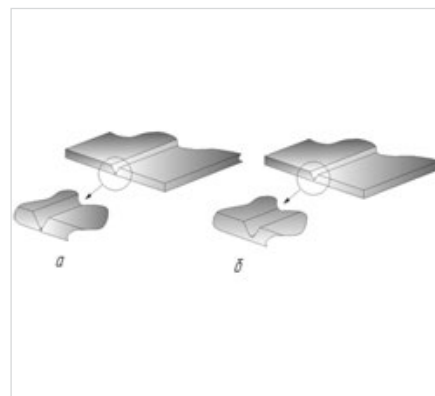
Общий вид образцов для проведения экспериментов по исследованию режимов сварки трубопроводов порошковыми проволоками. а) общий вид образца с V — образной разделкой для отработки режимов сварки корневого шва; б) общий вид образца с выборкой имитирующей готовый корневой шов сварного соединения магистрального трубопровода
